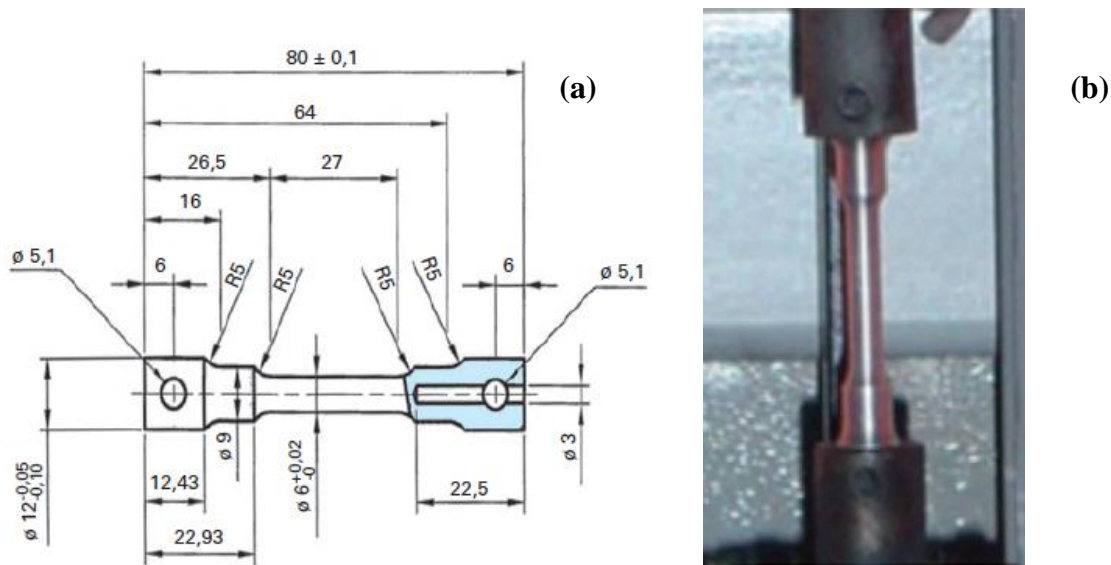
(a) Schéma de l'éprouvette de torsion (échelle en mm), (b) montage de l'éprouvette de torsion lors d'un essai à chaud
